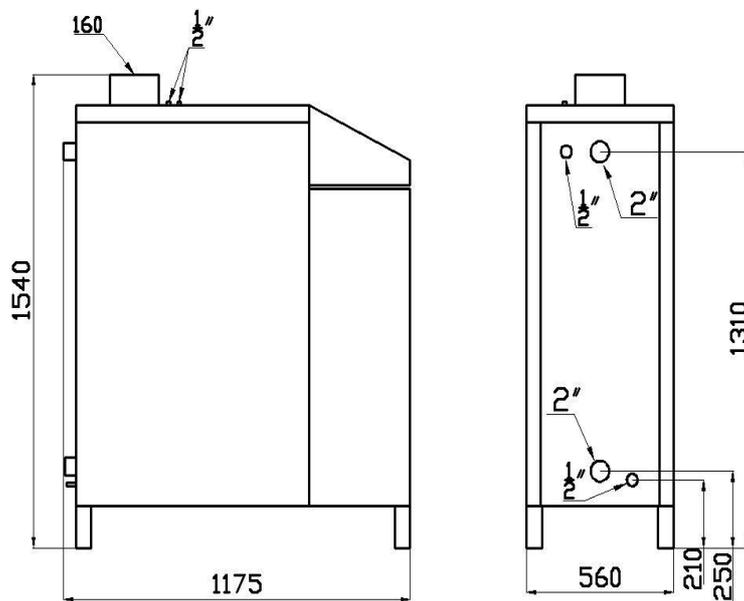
Kesselquerschnitt – Futura Pel-lets 25 und 35 kW
